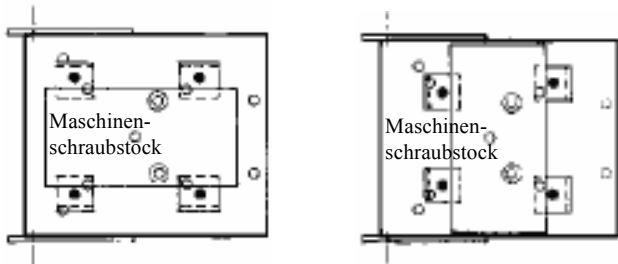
Befestigungspunkte für den Maschinschraubstock
